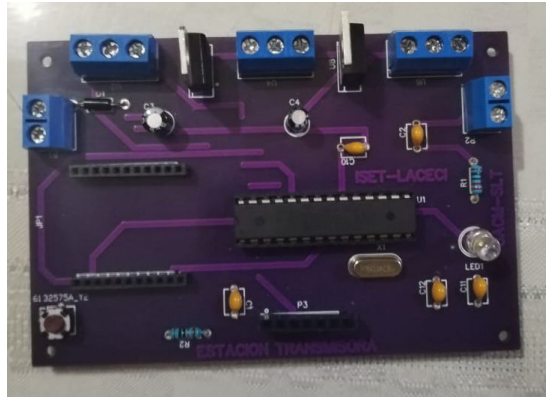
Placa emisora con sus componentes soldados
